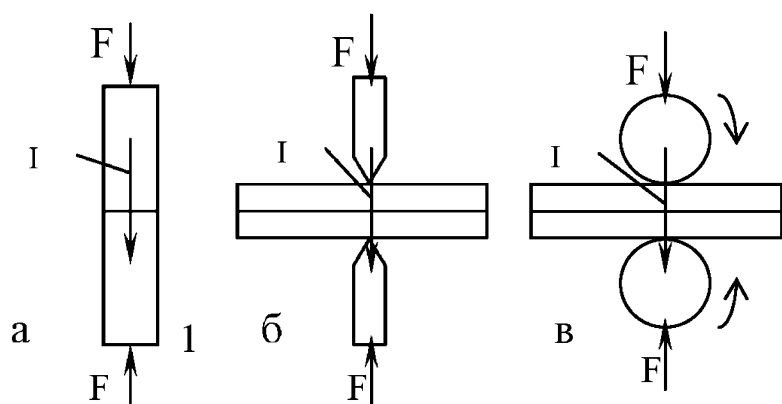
Основные виды контактной сварки: а – стыковая; б – точечная; в - роликовая.
